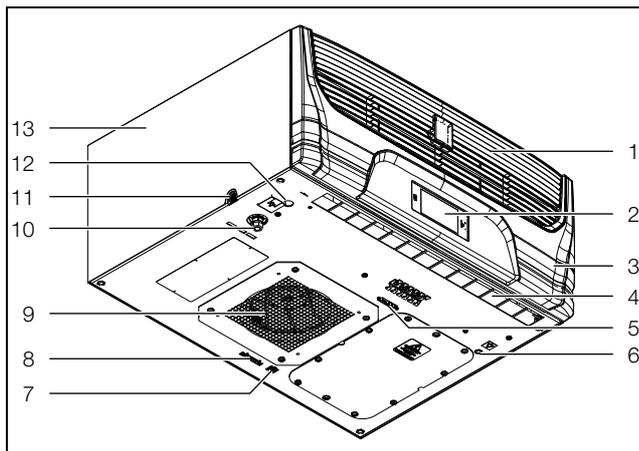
Hauptkomponenten des Dachaufbau-Kühlgeräts
